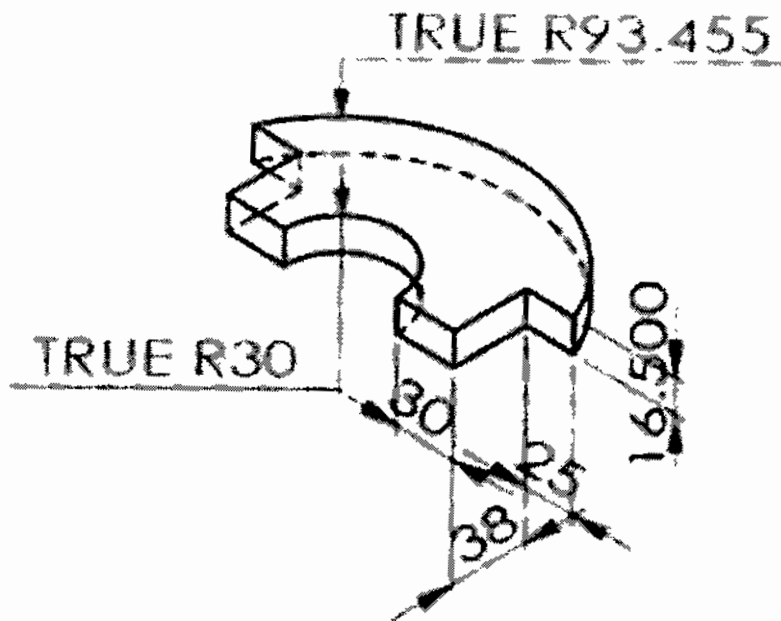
ภาพ drawing ของหัวแกรไฟต์
